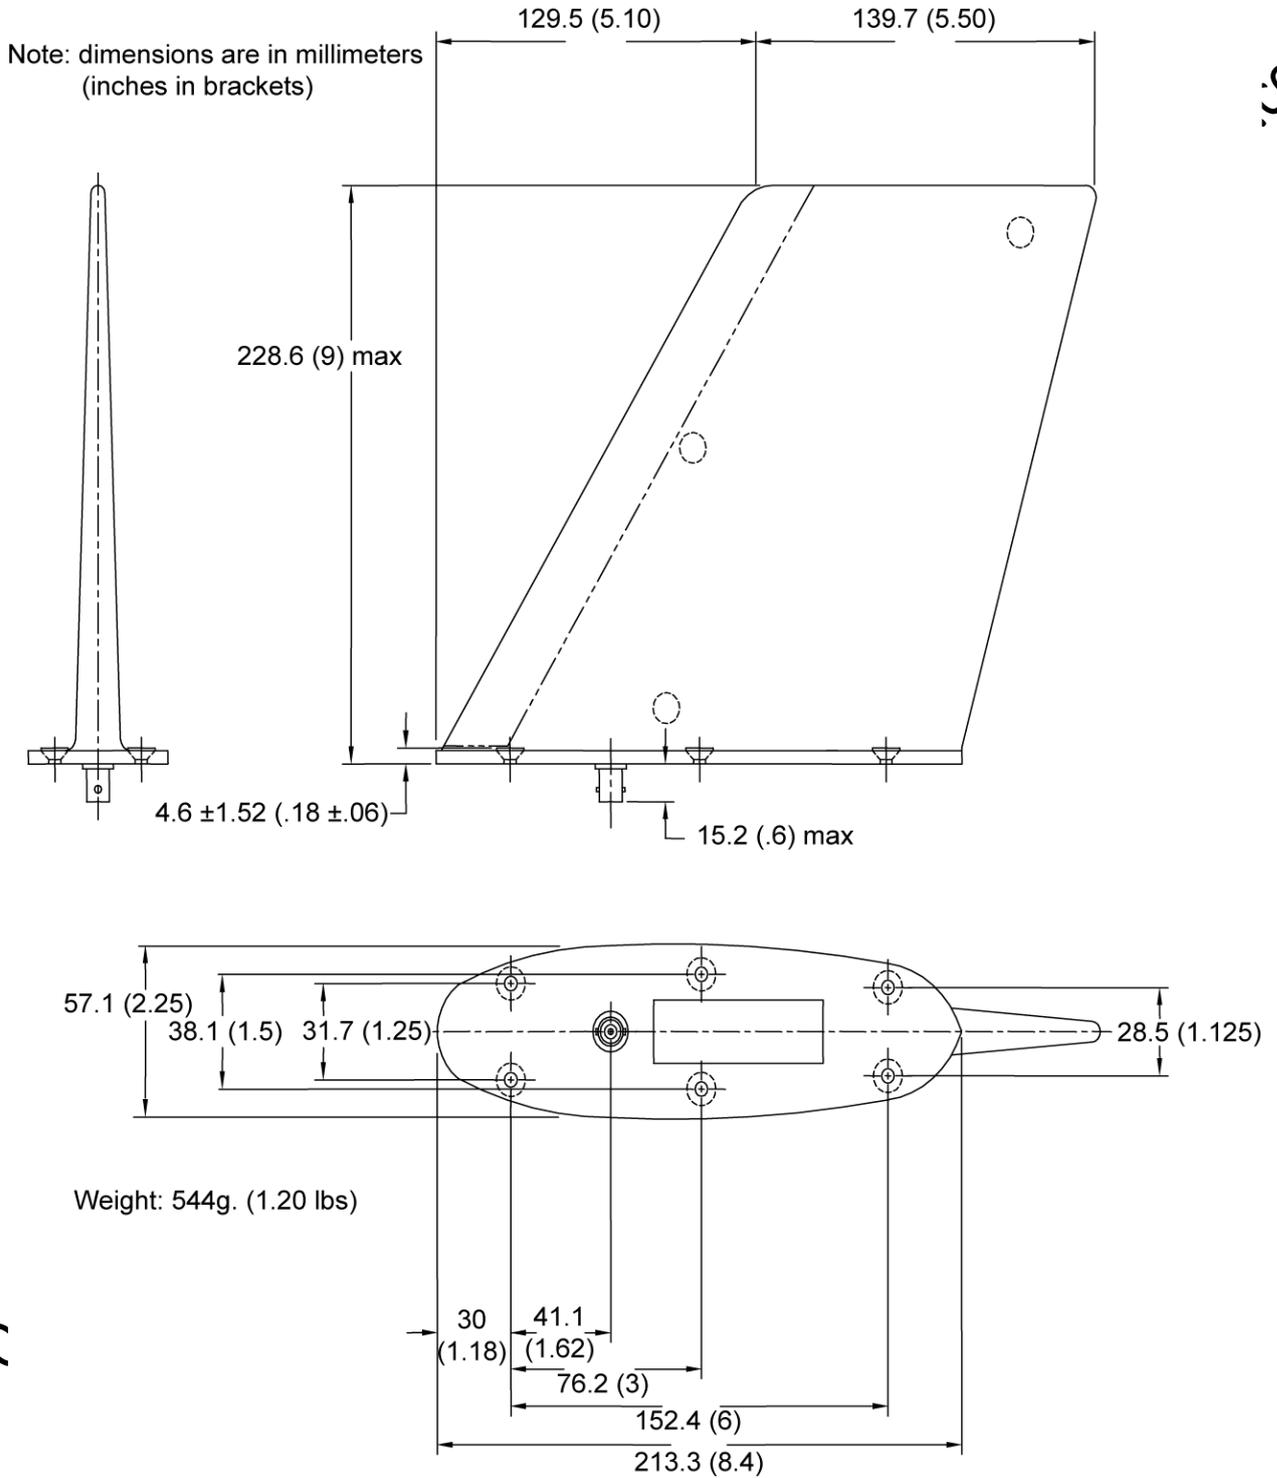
ANT560, Габаритные размеры, шаблон для сверления и вес
